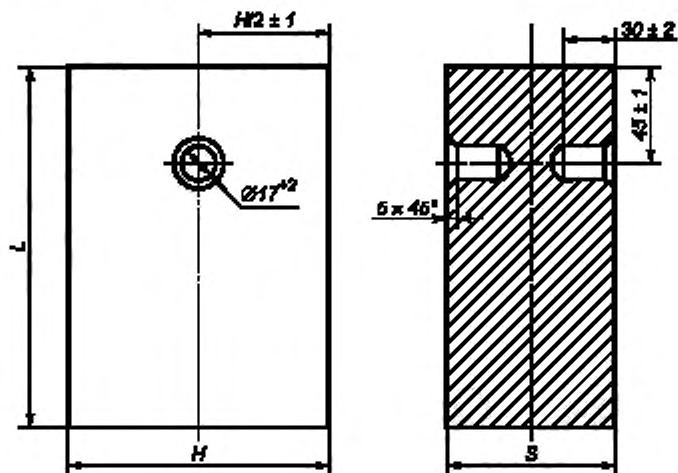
Размеры отверстий для штырей. Вариант 1
